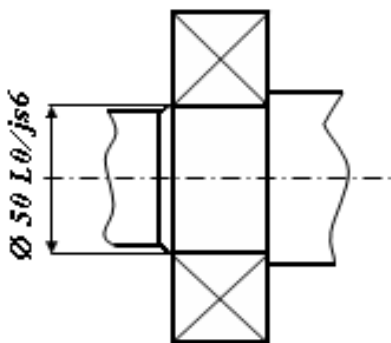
Обозначение посадки внутреннего кольца подшипника на вал
